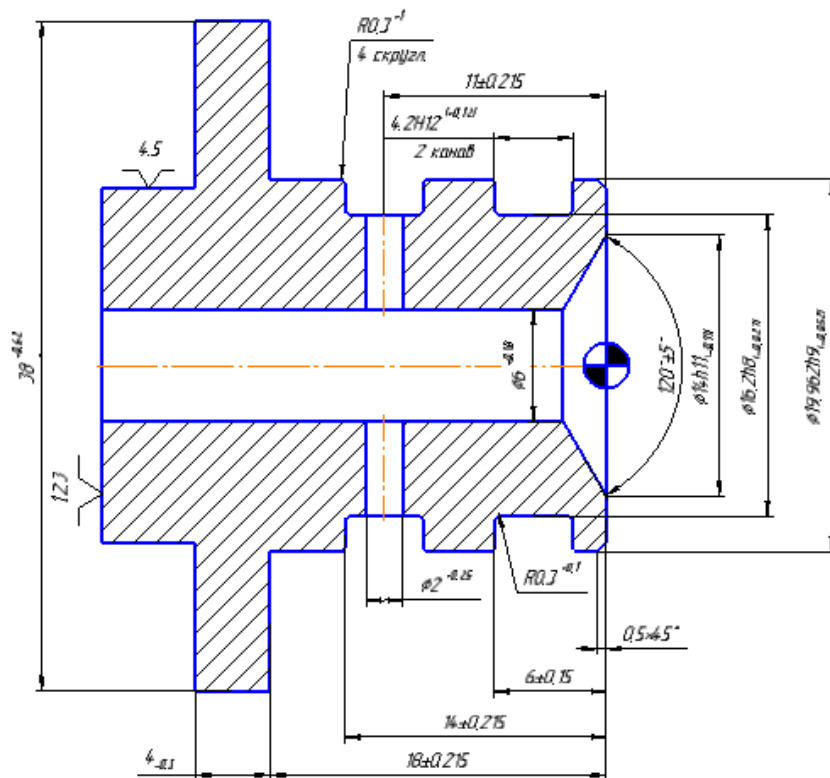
Схема базирования заготовки операция 010 установ А
